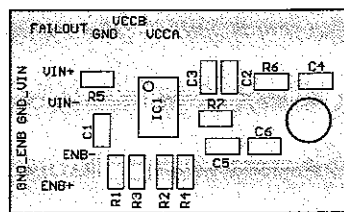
Die Platine für den MAX3263 wird nur mit SMD-Bauelementen bestückt.
